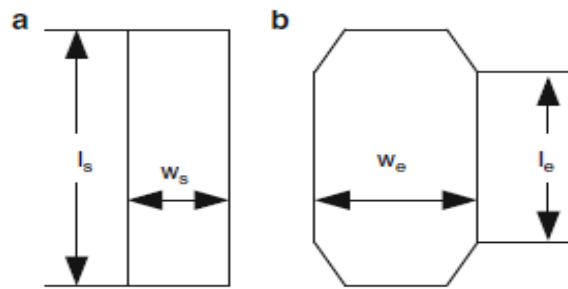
Forme de la fente : (a) original ; (b) après expansion
